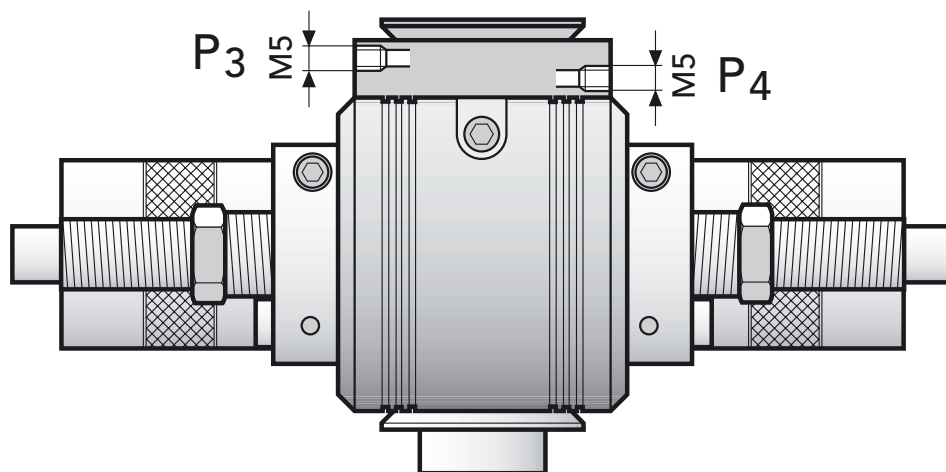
Alimentazione d'aria compressa DAP-2 / DAPI-2
